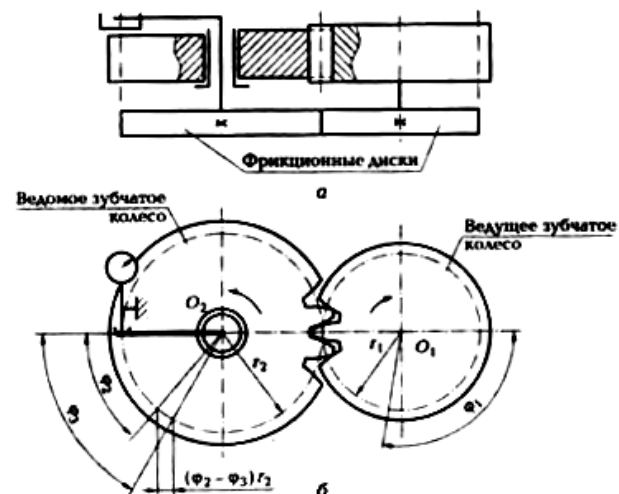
Схема комплексного контроля цилиндрической зубчатой передачи:
